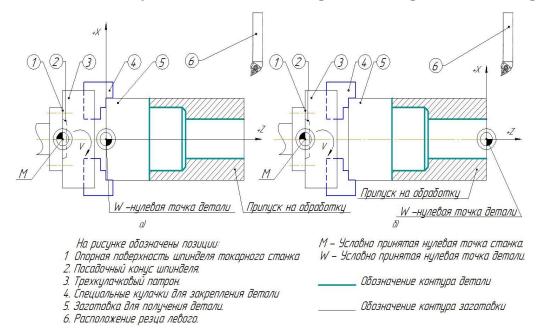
Задание нулевой точки детали при верхнем расположении резца;
